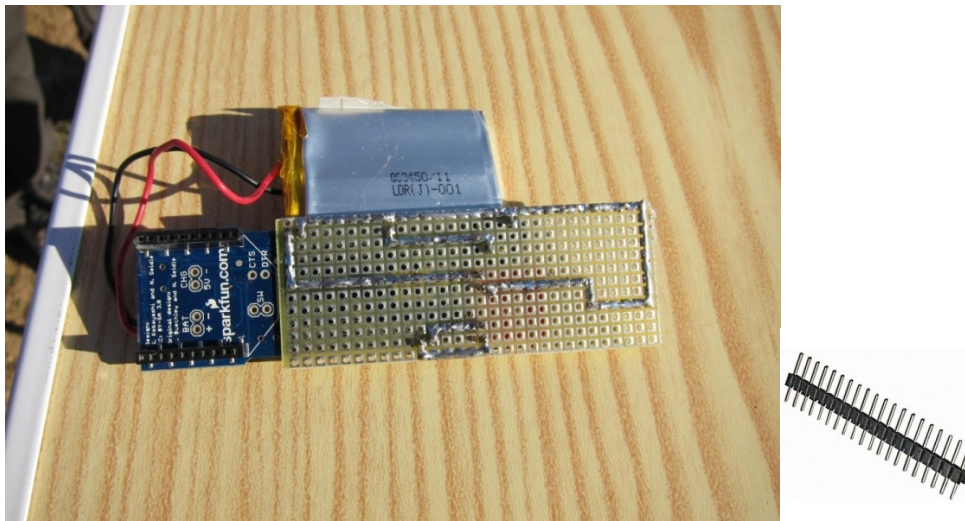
Imagen de las pistas soldadas. A la derecha pines usados para afianzar la soldadura.
